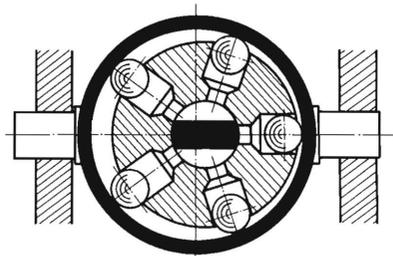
Schema einer Radialkolbenmaschine mit Kugelkolben.
